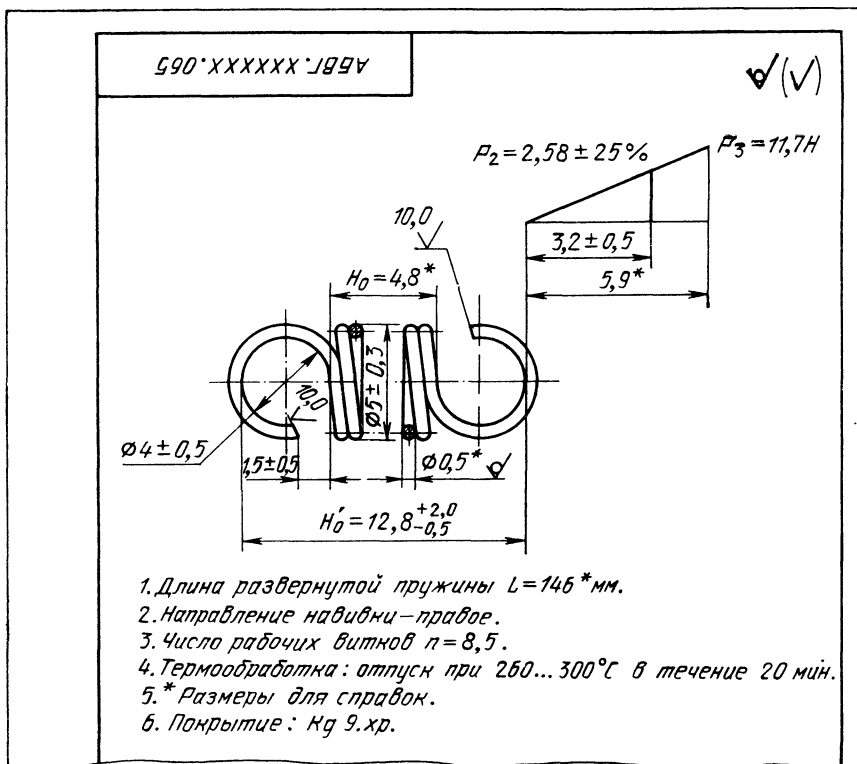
Рабочий чертеж винтовой пружины растяжения
